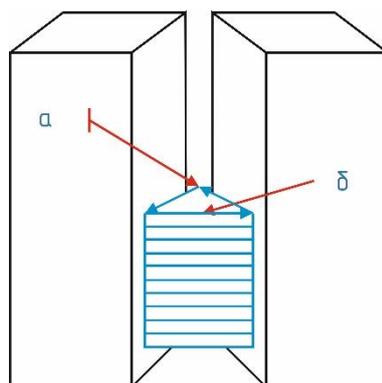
Сварка корневого шва в разделке кромок треугольником
